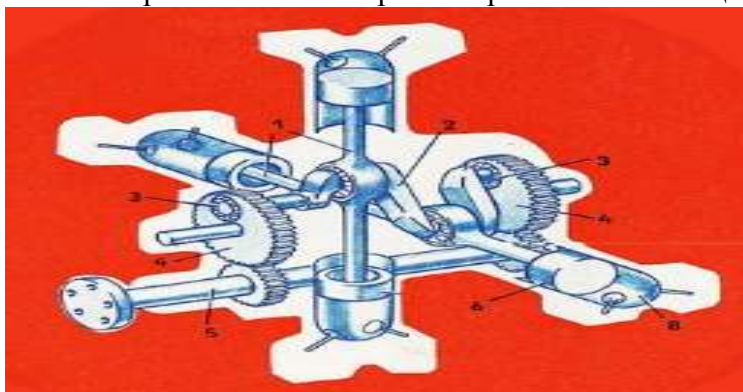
Принципиальное устройство бесшатунного двигателя: 1 — поршневой шток; 2 — коленчатый вал; 3 — подшипник кривошипа; 4 — кривошип; 5 — вал отбора мощности; 6 — поршень; 7 — ползун штока; 8 — цилиндр.
